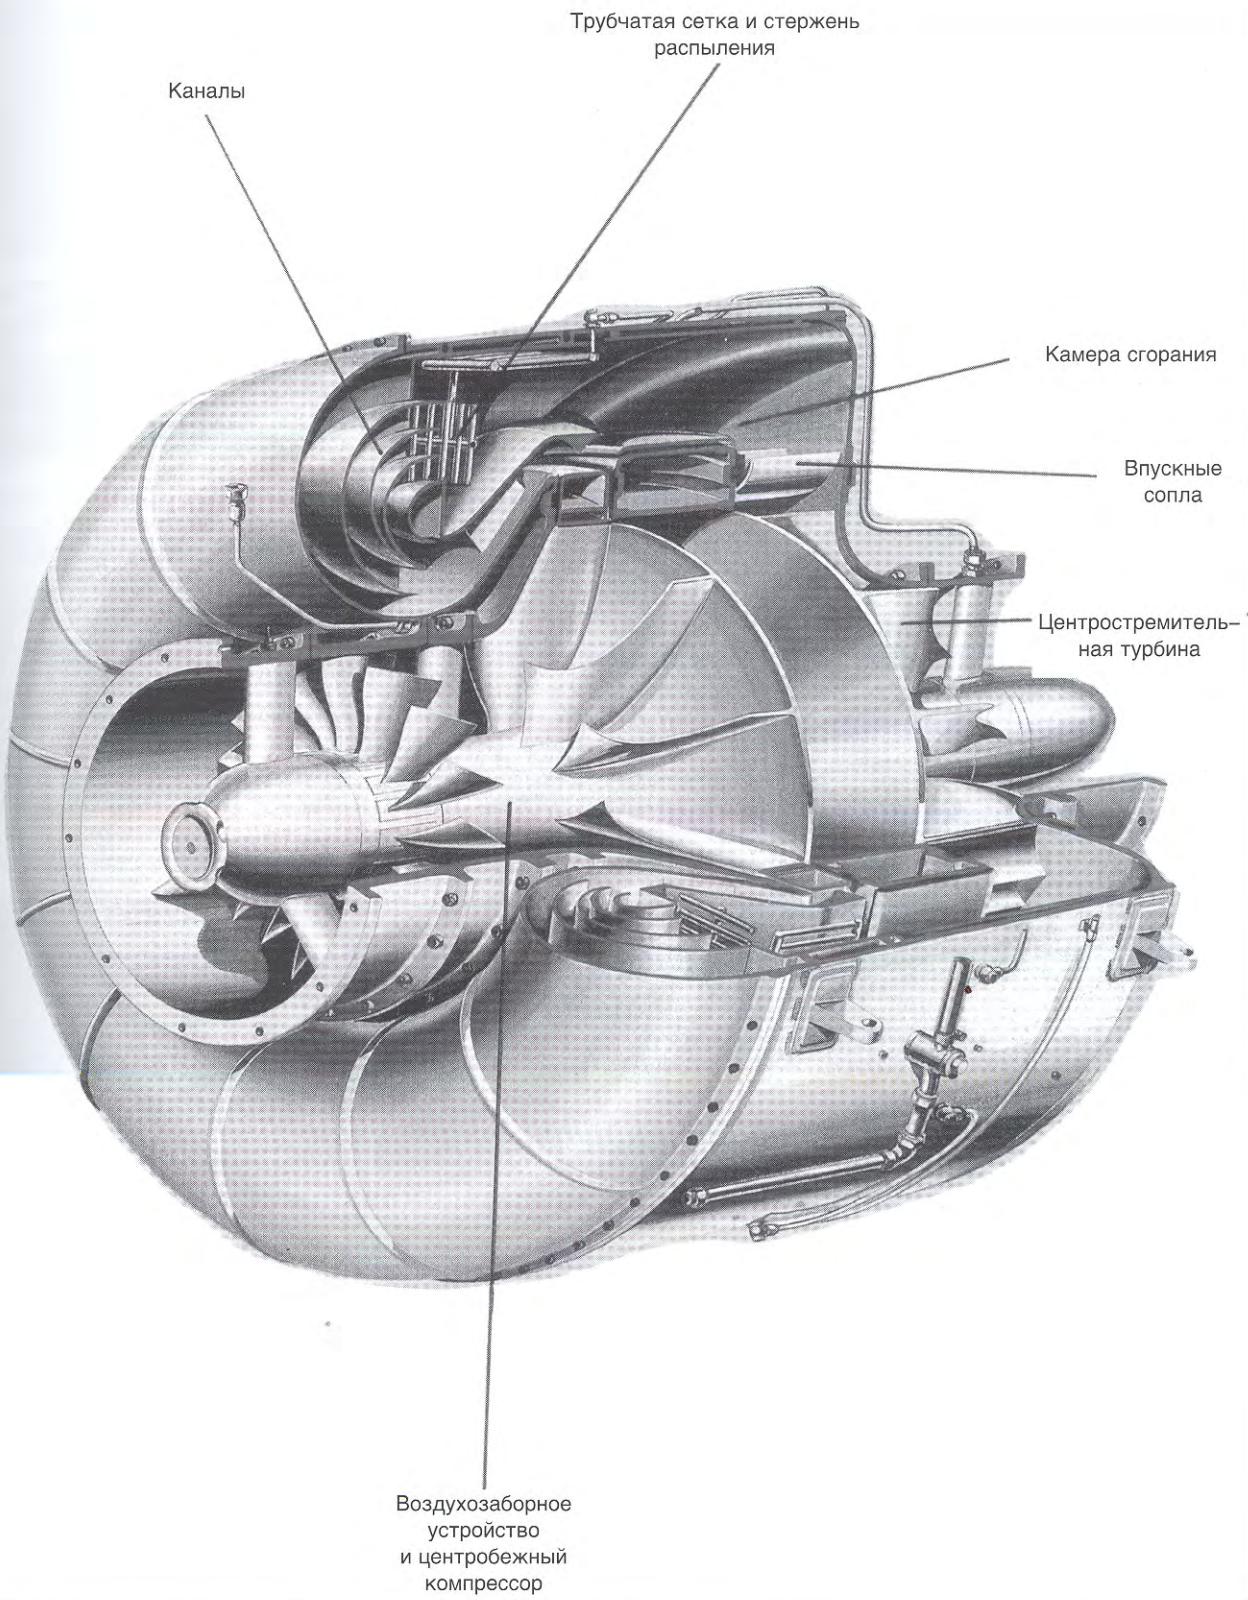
Турбореактивный двигатель HeS 3b (схема получена от Билла Ганстона)
